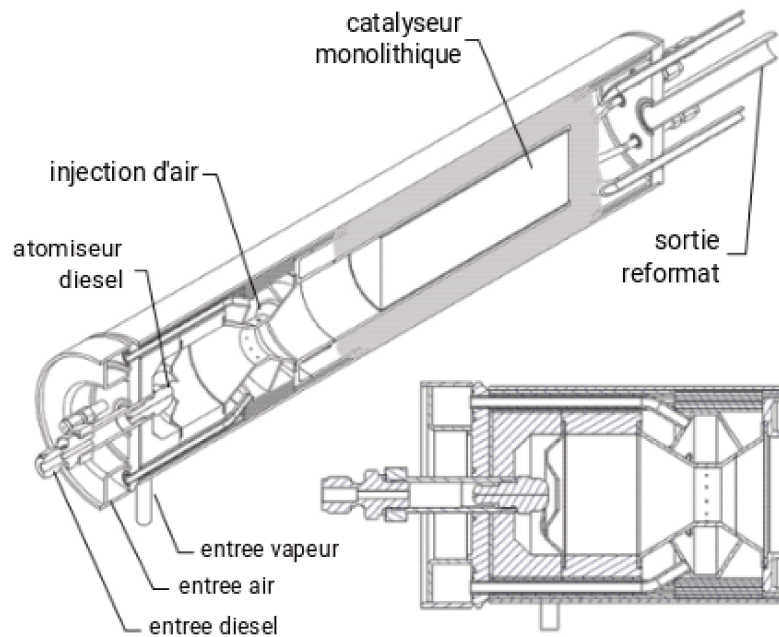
Vue en coupe du reformeur autothermique au diesel ATR 7, d'après [52].
